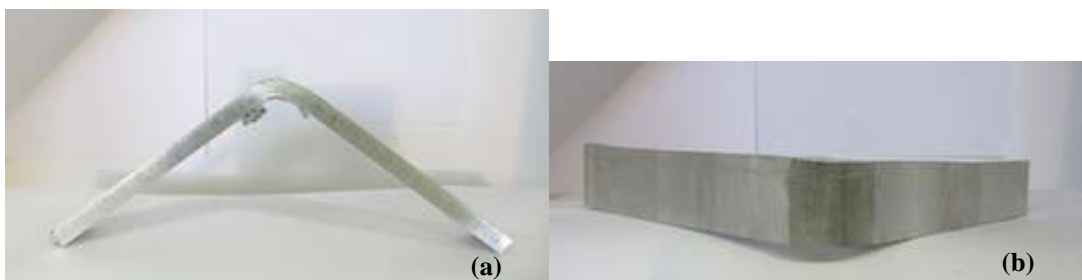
Teste de dobramento na junta dissimilar soldada por FSW. (a) Vista da espessura da junta. (b) Vista superior da junta ensaiada.
